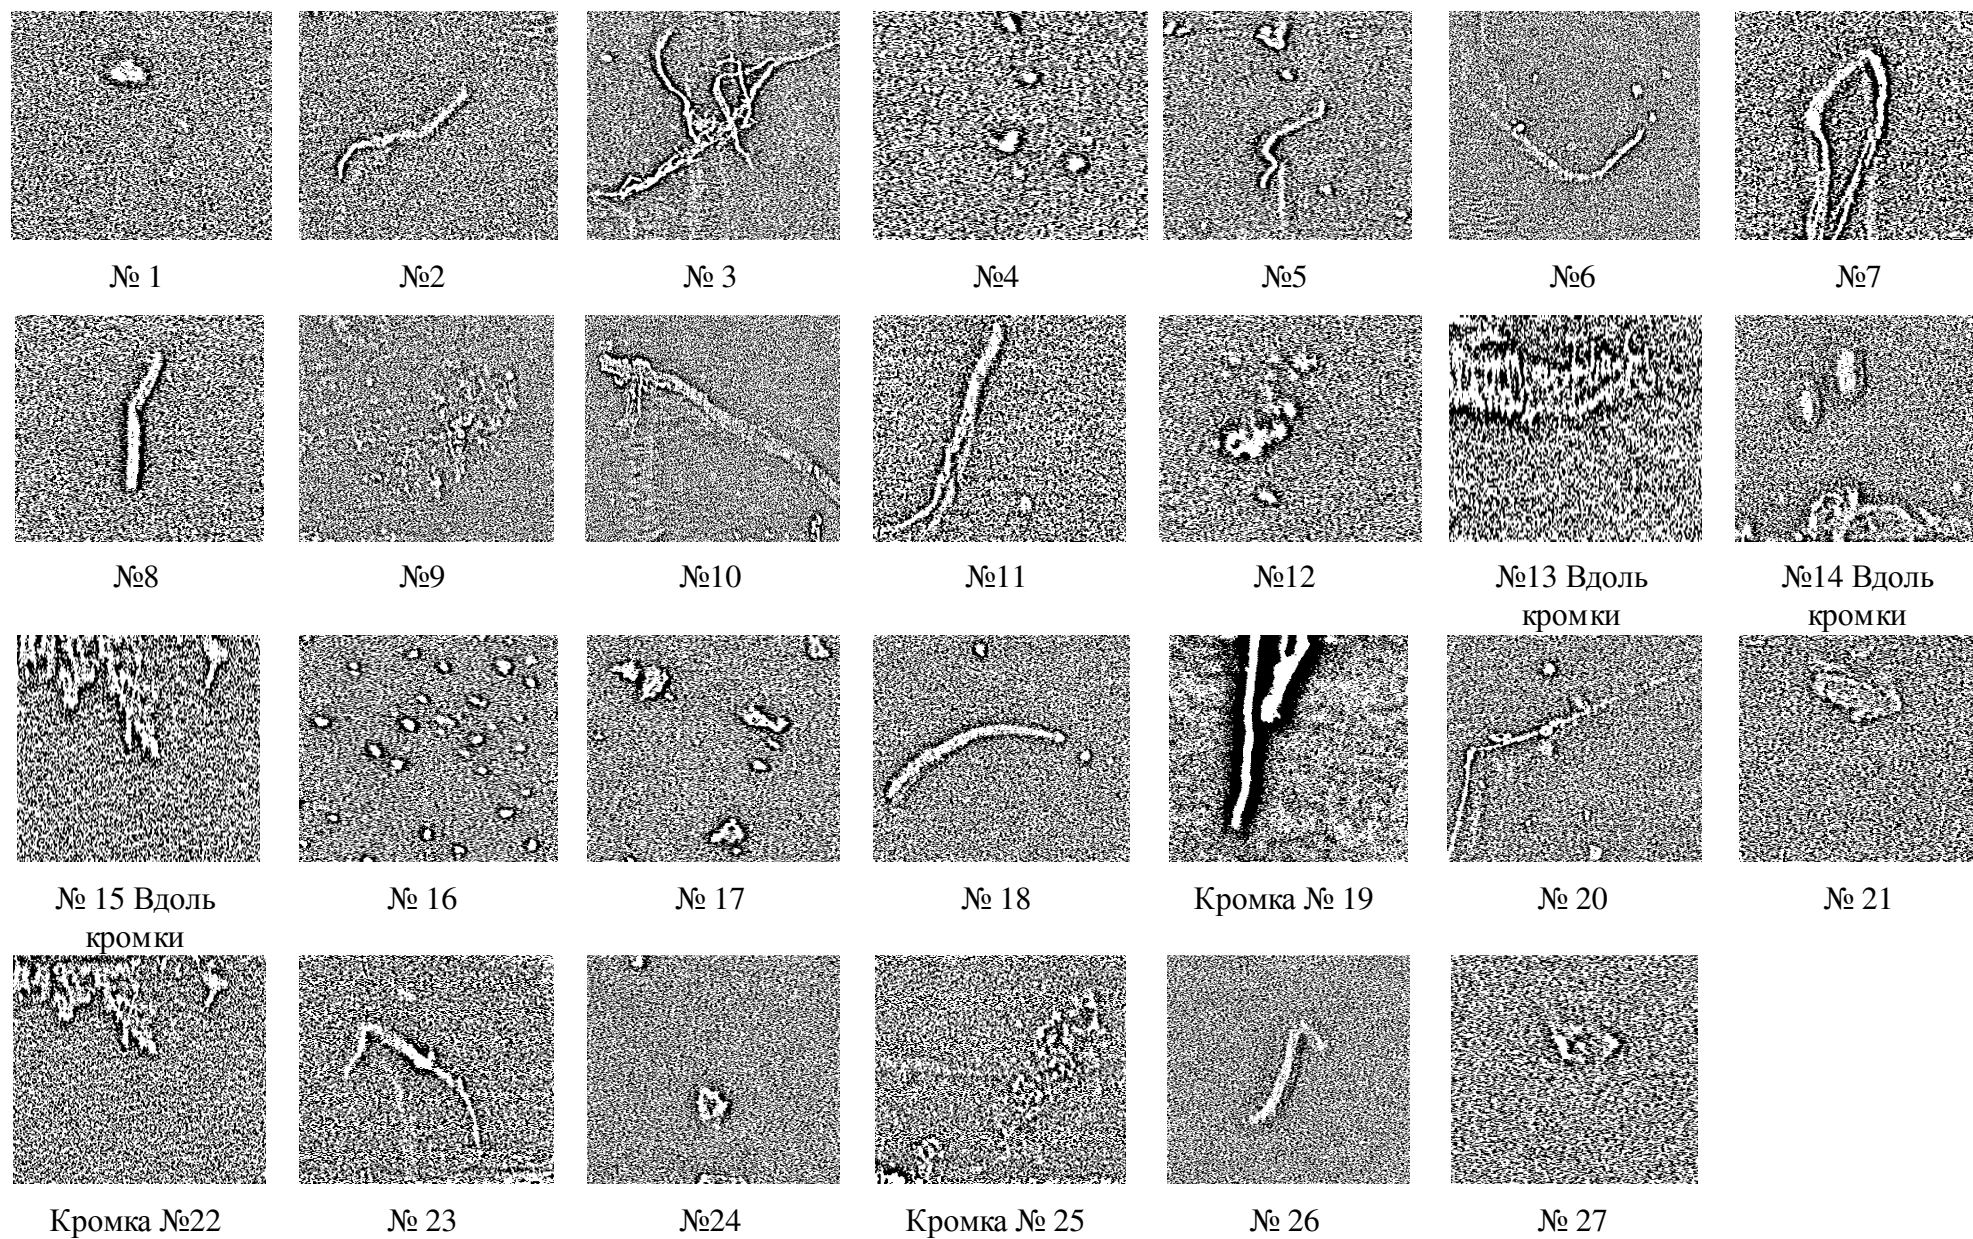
Дефекты на поверхности дорожки качения колец подшипников после шлифования
